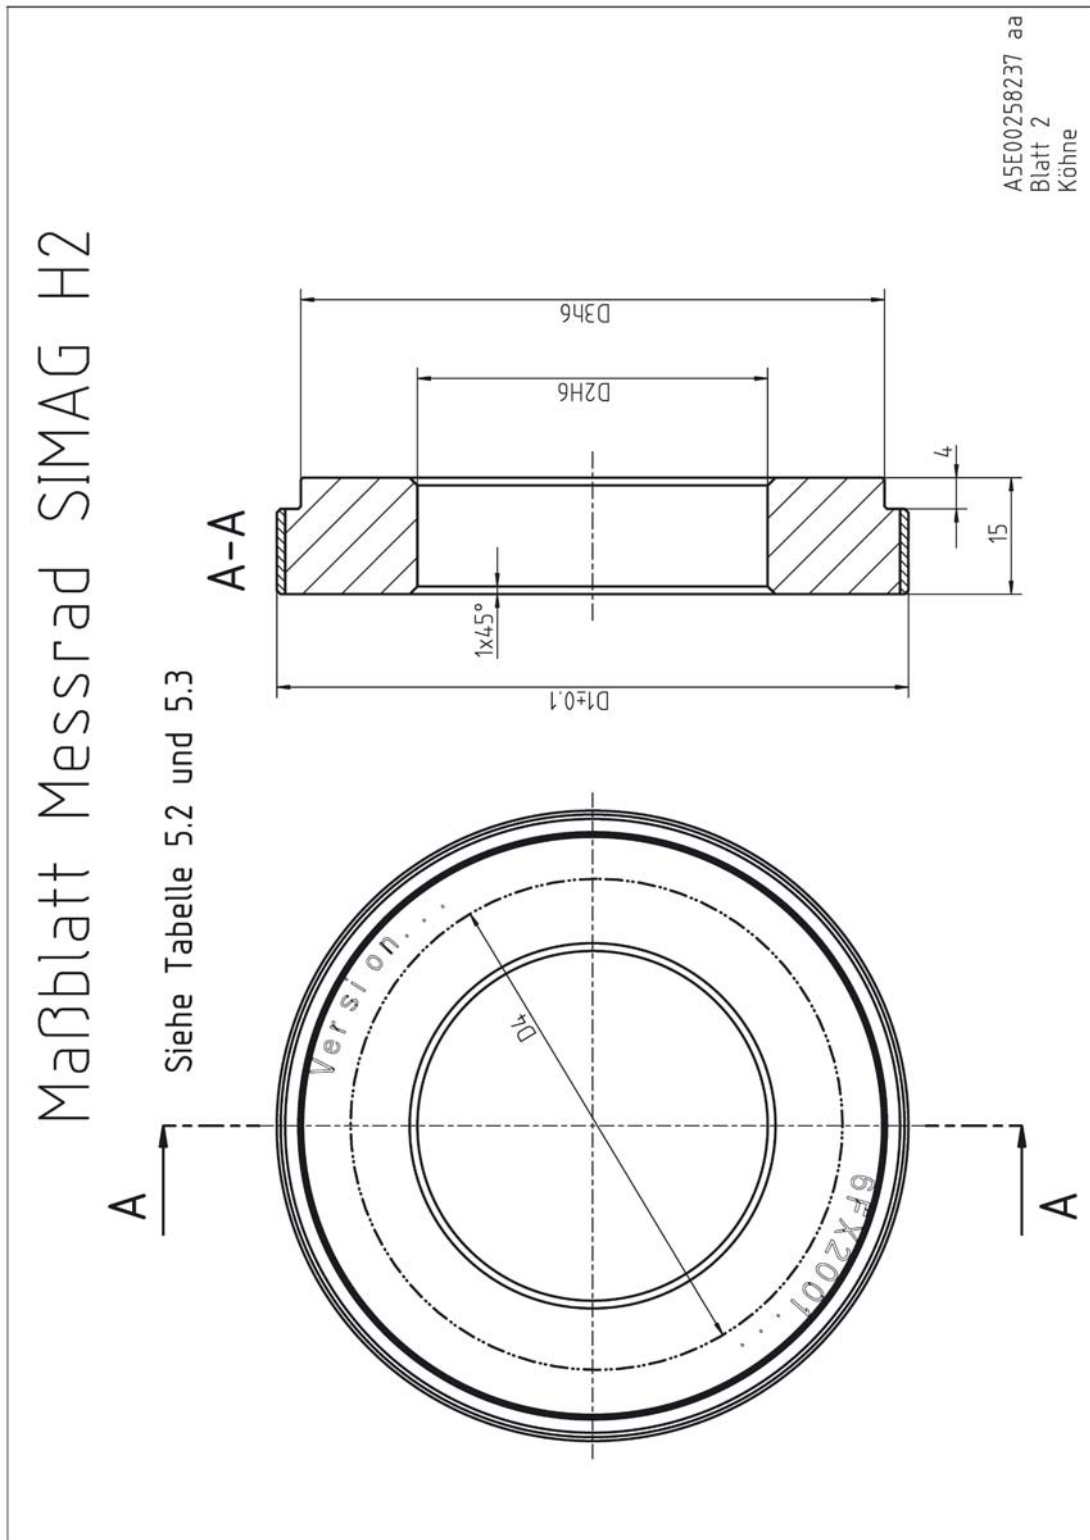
Габаритный чертеж магнитного обода SIMAG H2
